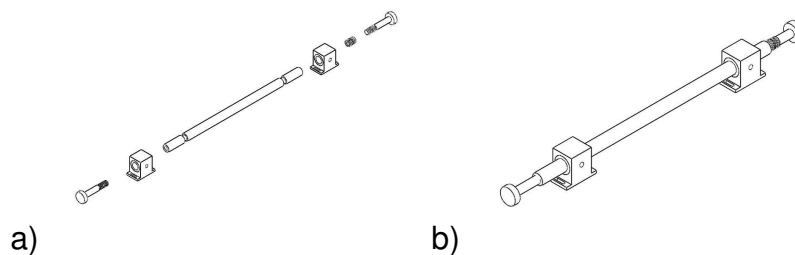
a) Vista explosionada del subensamble, b) Subensamble completo del seguro para la platina.
